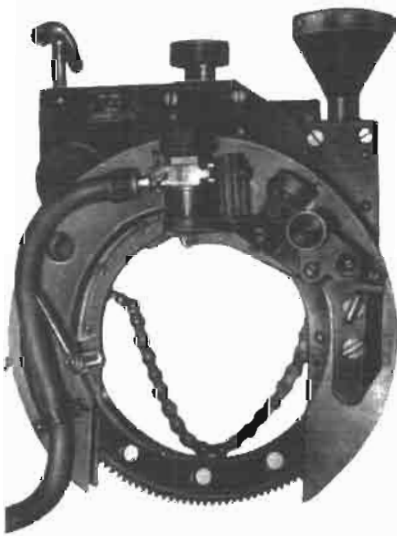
Головки ОДА-1, ОДА-2 и ОДА-3 для орбитальной сварки последовательным проплавлением и с автоопрессовкой труб диаметром 8...26, 20...42 и 42...76 мм соответственно
